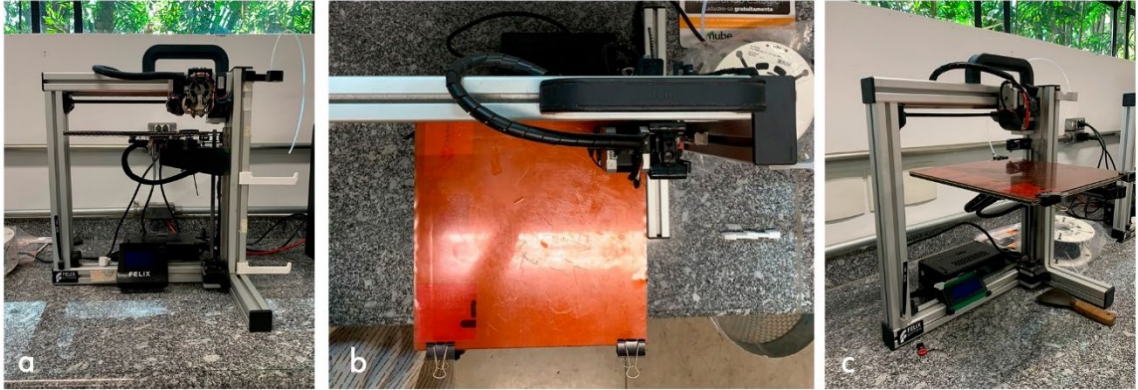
Impressora FELIX Printer 3.0, imagem frontal (a), mesa de impressão (b) e isométrica (c). Fonte: Autora
